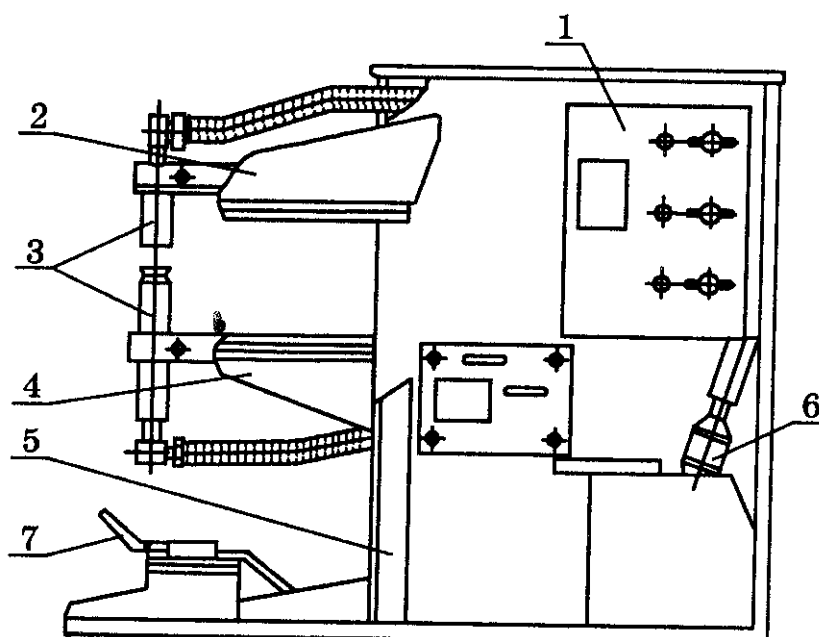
Машина для точечной сварки МТ-601
